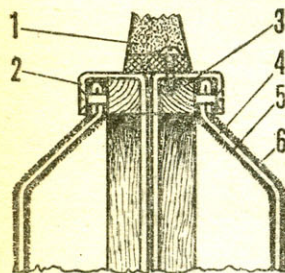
Детали конструкции чемоданчика: 1 — ручка, 2 — дюралюминиевый швеллер, 3 — деревянный вкладыш, 4 — алюминиевый противень, 5 — внутренняя матерчатая обтяжка, 6 — искусственная кожа.
